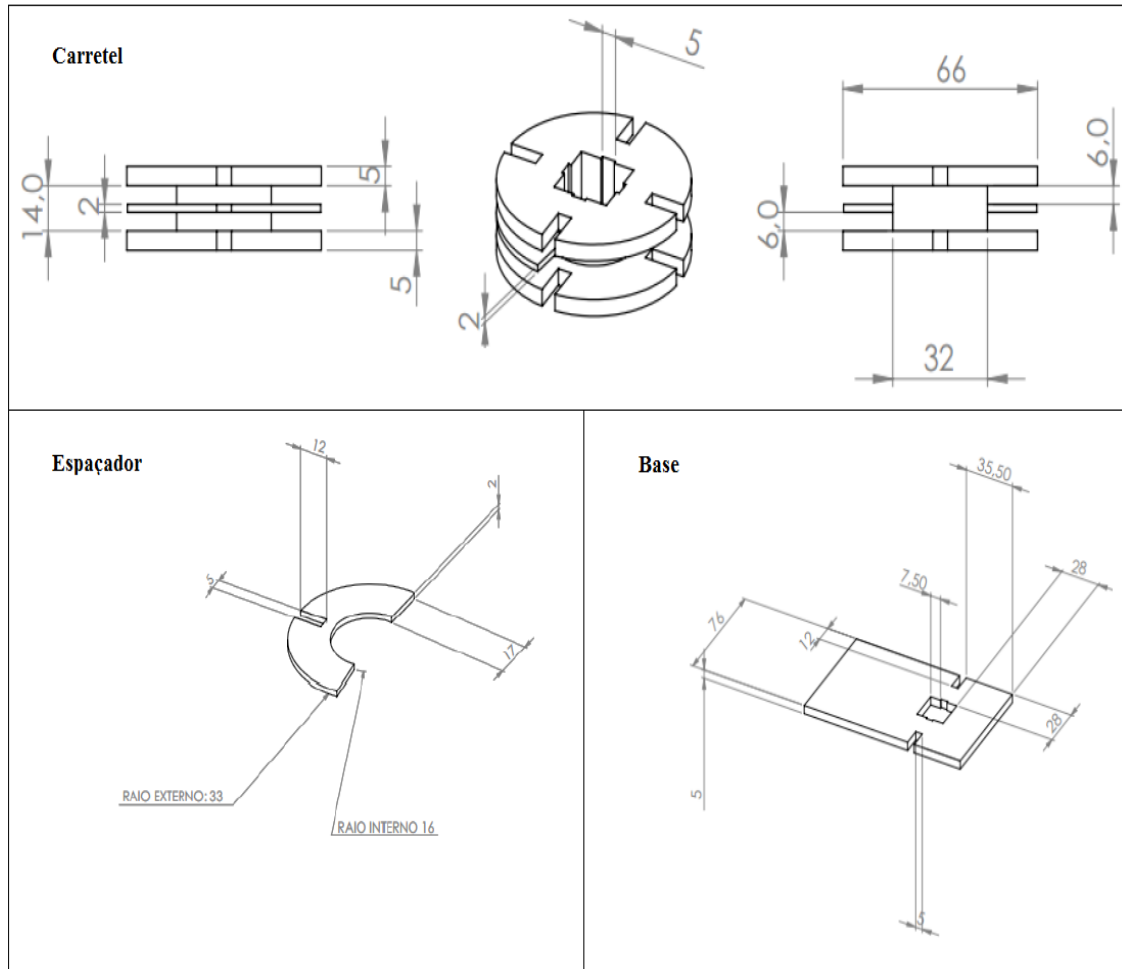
Projeto do carretel das bobinas de panqueca dupla. Adaptada de [63].
